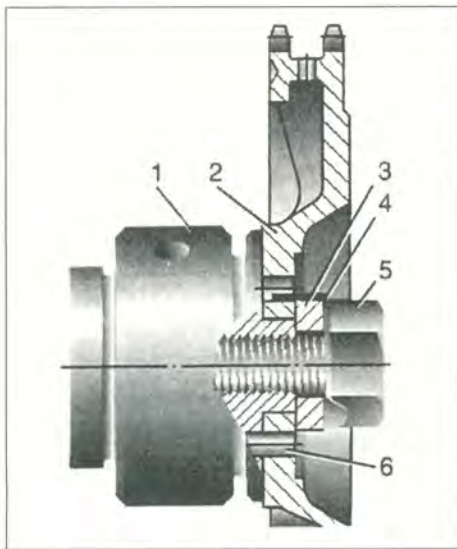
"Штатная" конструкция соединения распределительного вала и звездочки: 1 – распредвал; 2 – звездочка; 3 – опорная шайба; 4 – контрольная (фиксирующая) шайба; 5 – центральный болт; 6 – штифт.
